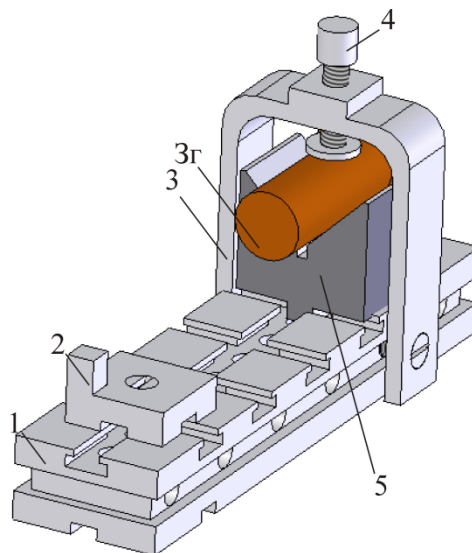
Общий вид конструкции УСП: 1 – базовая плита; 2 – установ; 3 – хомутик; 4 – винтовой зажим; 5 – призма
